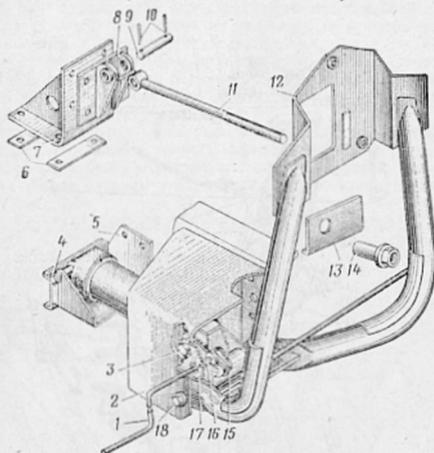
Держатель запасного колеса шасси Урал-375А:
